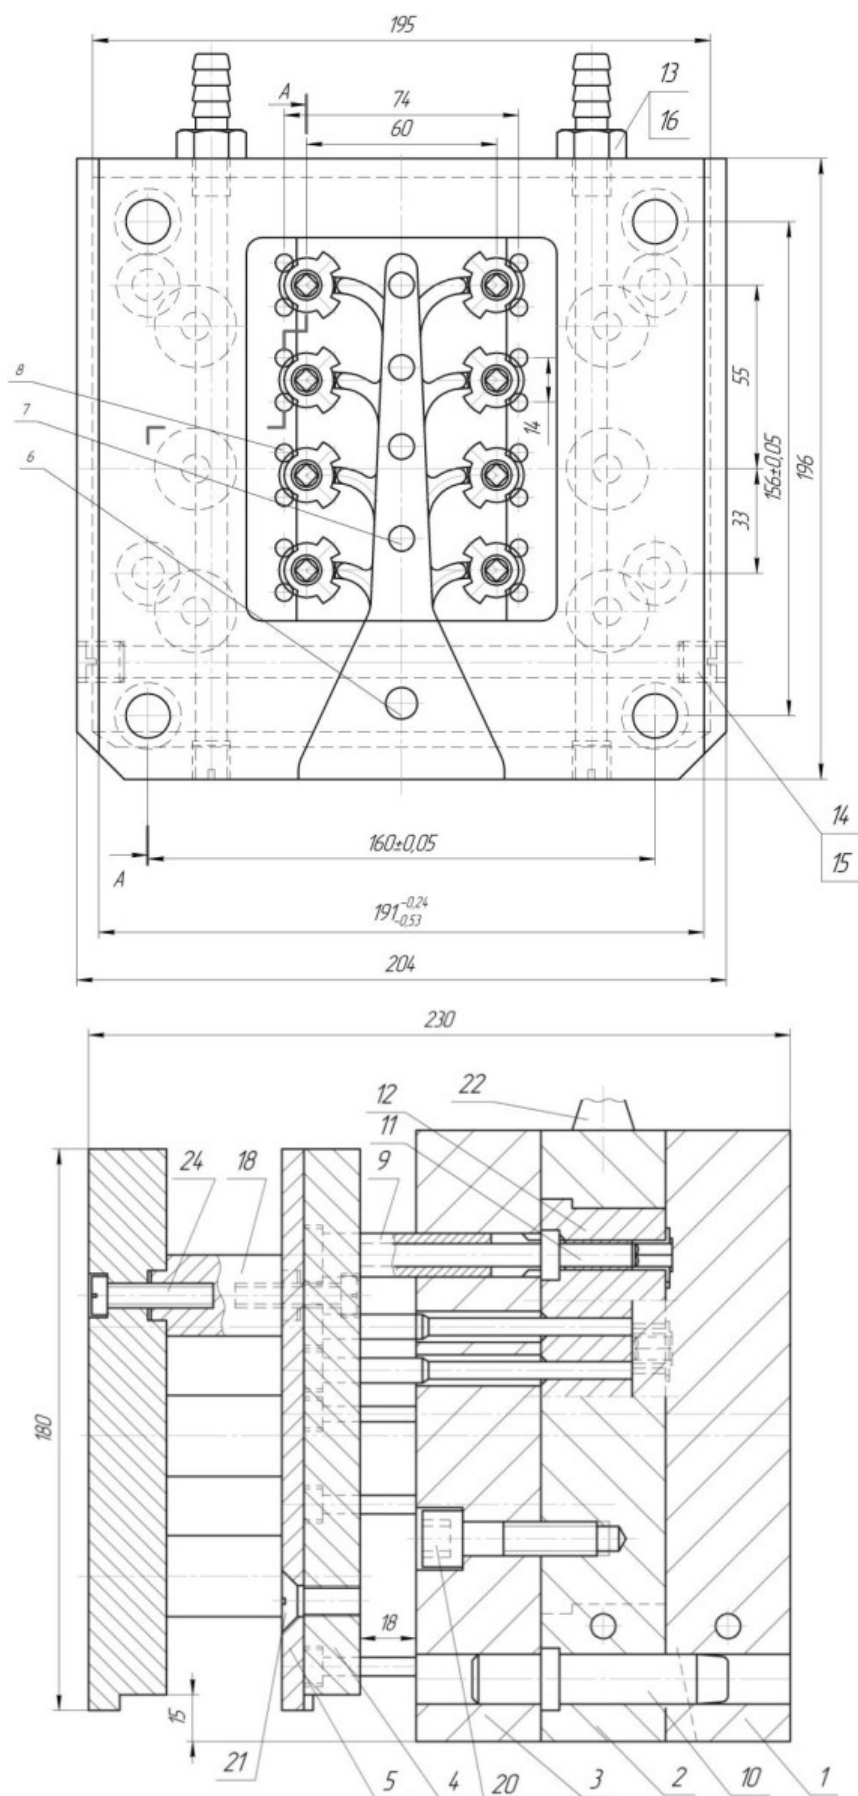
Фрагмент конструкції прес-форми для виготовлення заготовки кришки батареї
